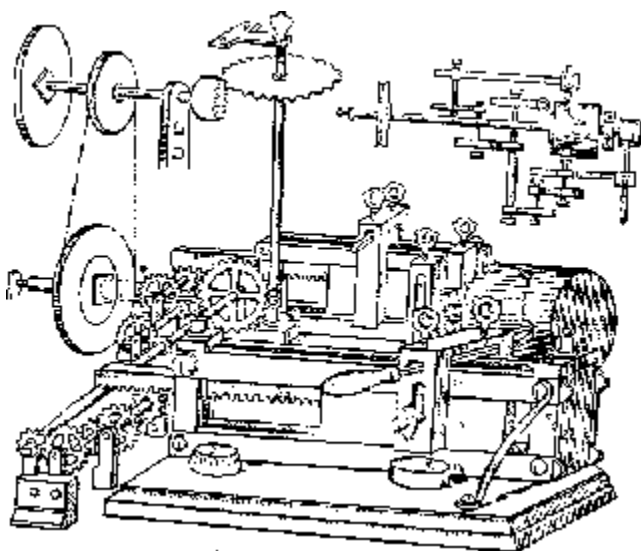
Кинематическая схема токарно-копировального станка А. К. Нартова, 1712 г.
